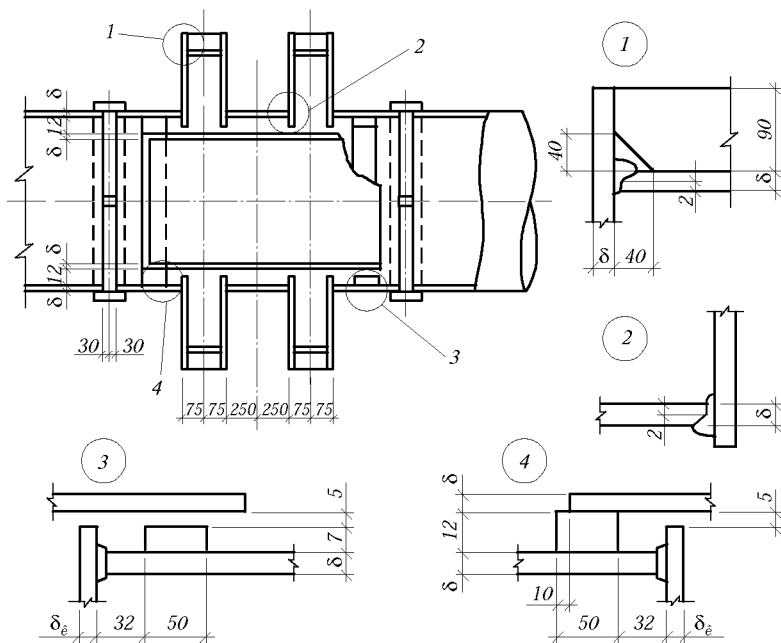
Сварной дисковый компенсатор: 1–4 – узлы
